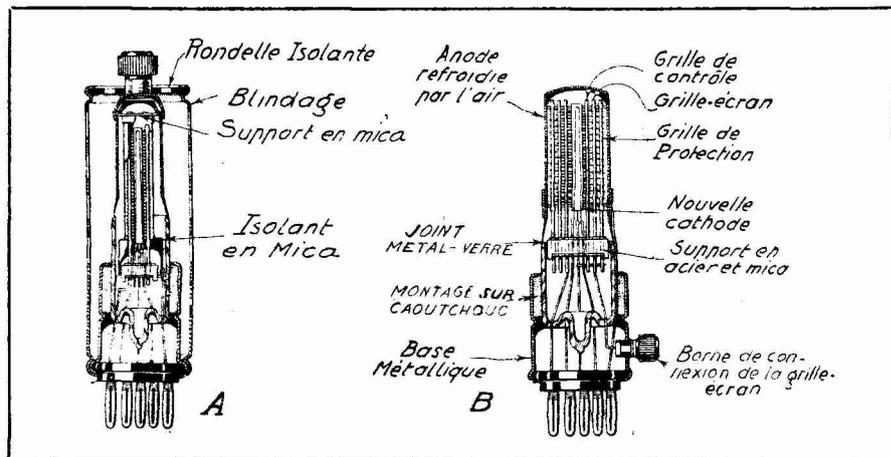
La lampe Catkin à grille-écran et la trigrille.
